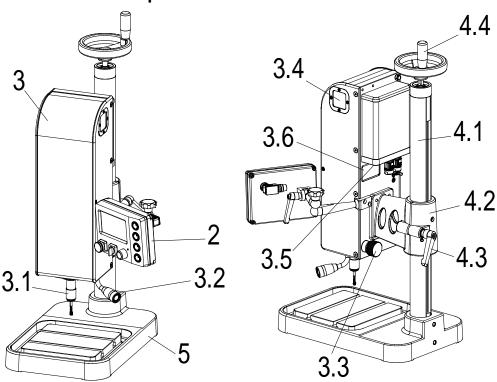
Vue avant et arrière de la machine à fileter avec unité de commande
